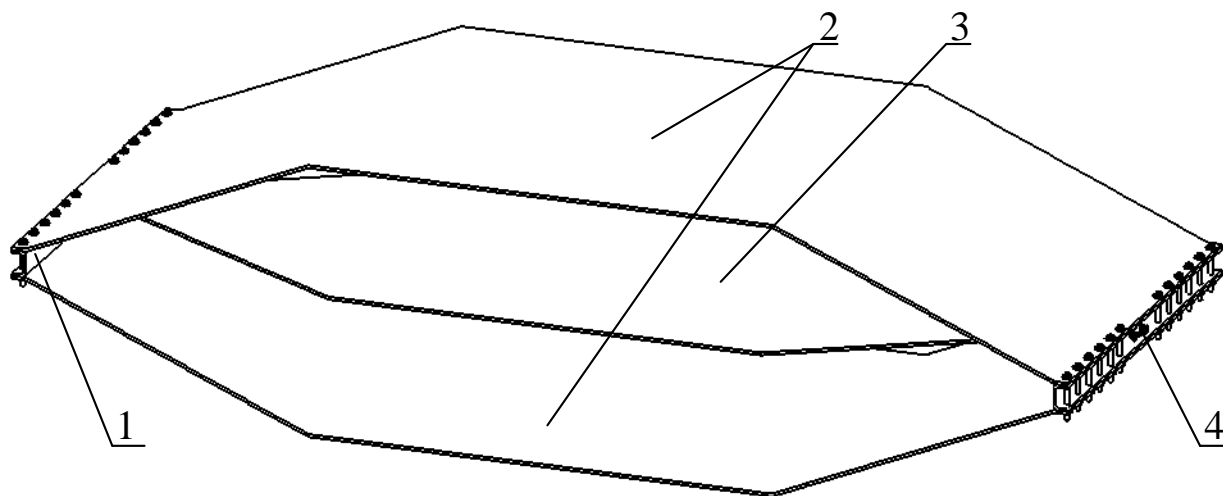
Диметрический вид твердотельной модели ТЕМ-камеры открытого исполнения: 1 – П-образный соединитель, 2 – корпус, 3 – центральный проводник, 4 – СВЧ-соединитель
